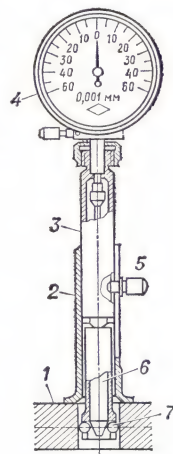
Шариковый индикаторный нутромер для измерения малых отверстий: 1 — деталь; 2 — упор; 3 — измерительная вставка; 4 — отсчётное устройство; 5 — закрепительный винт; 6 — игла; 7 — измерительный шарик.
